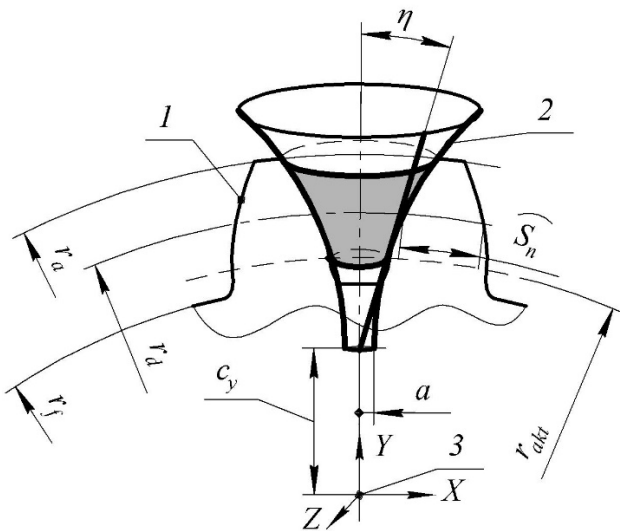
Розрахункова схема визначення параметрів ВІП пальцевої фрези на базі гіперболоїда: 1 – зубчасте колесо, 2 – поверхня гіперболоїда, 3 – вісь колеса
